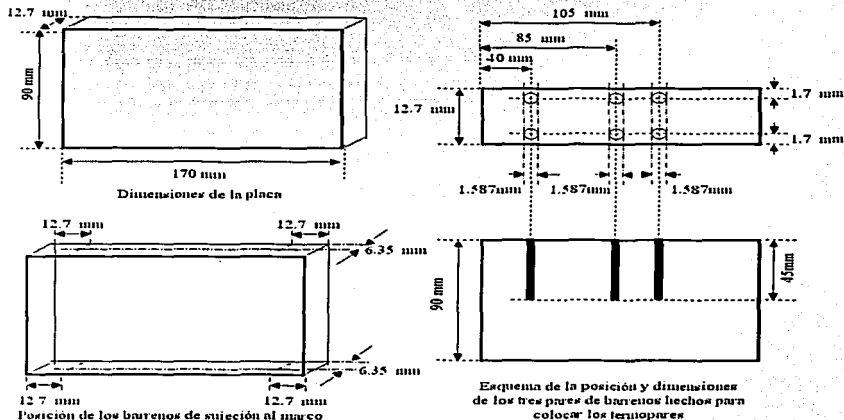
Dimensiones de la placa de prueba y la posición de cada barreno para termopar y sujeción.
